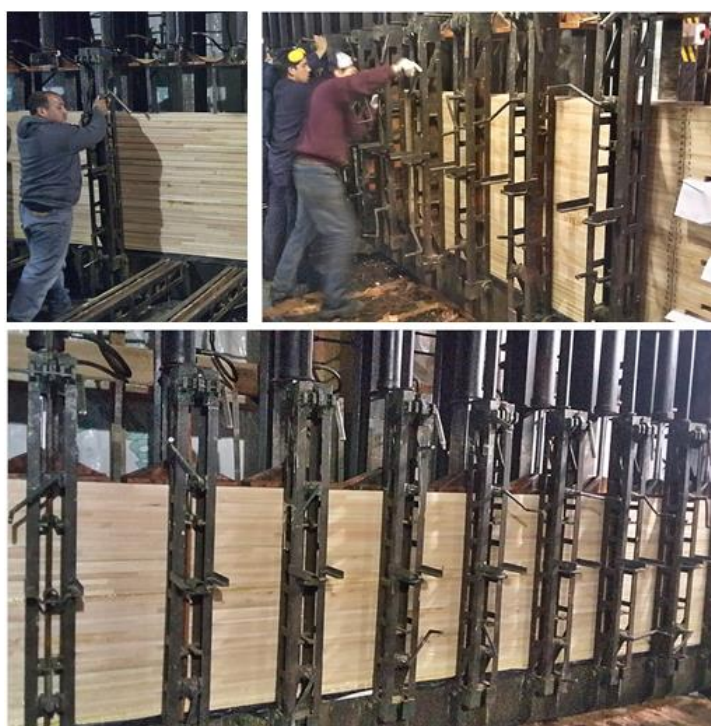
Máquina de prensado de vigas laminadas encoladas.
